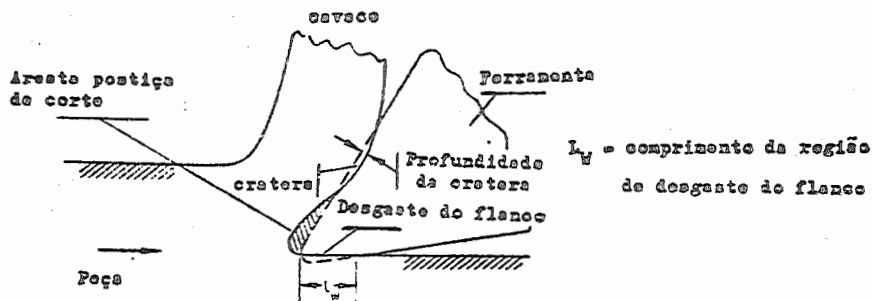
Região de desgaste progressivo durante a usinagem.
